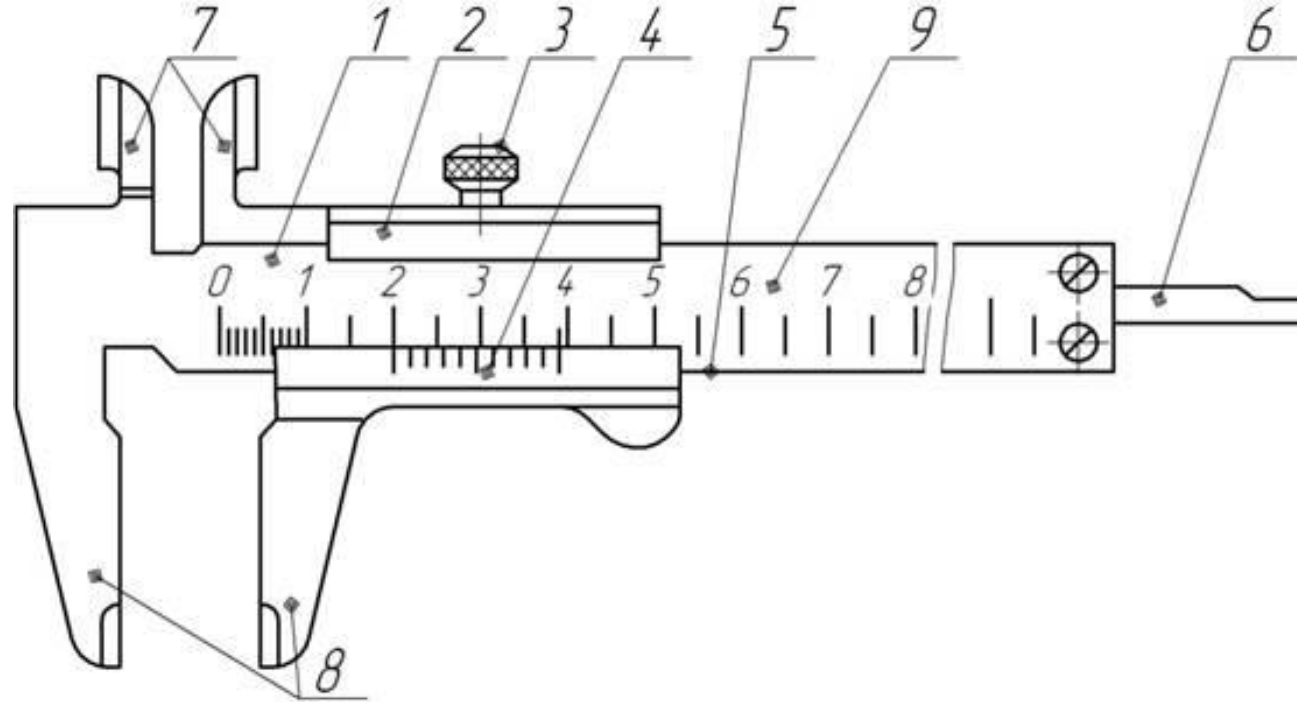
Конструкція та будова штангенциркуля ШЦ-I: 1 – штанга; 2 – рамка; 3 – фіксатор; 4 – ноніус; 5 – робоча поверхня штанги; 6 – глибиномір; 7 – губки з вимірювальними поверхнями кромки для вимірювання внутрішніх розмірів; 8 – губки з плоскими вимірювальними поверхнями для вимірювання зовнішніх розмірів; 9 – шкала штанги
